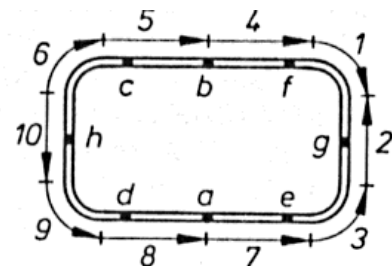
Heft- und Schweißfolge; Heftfolge a-h, Schweißfolge 1-10, /1/
